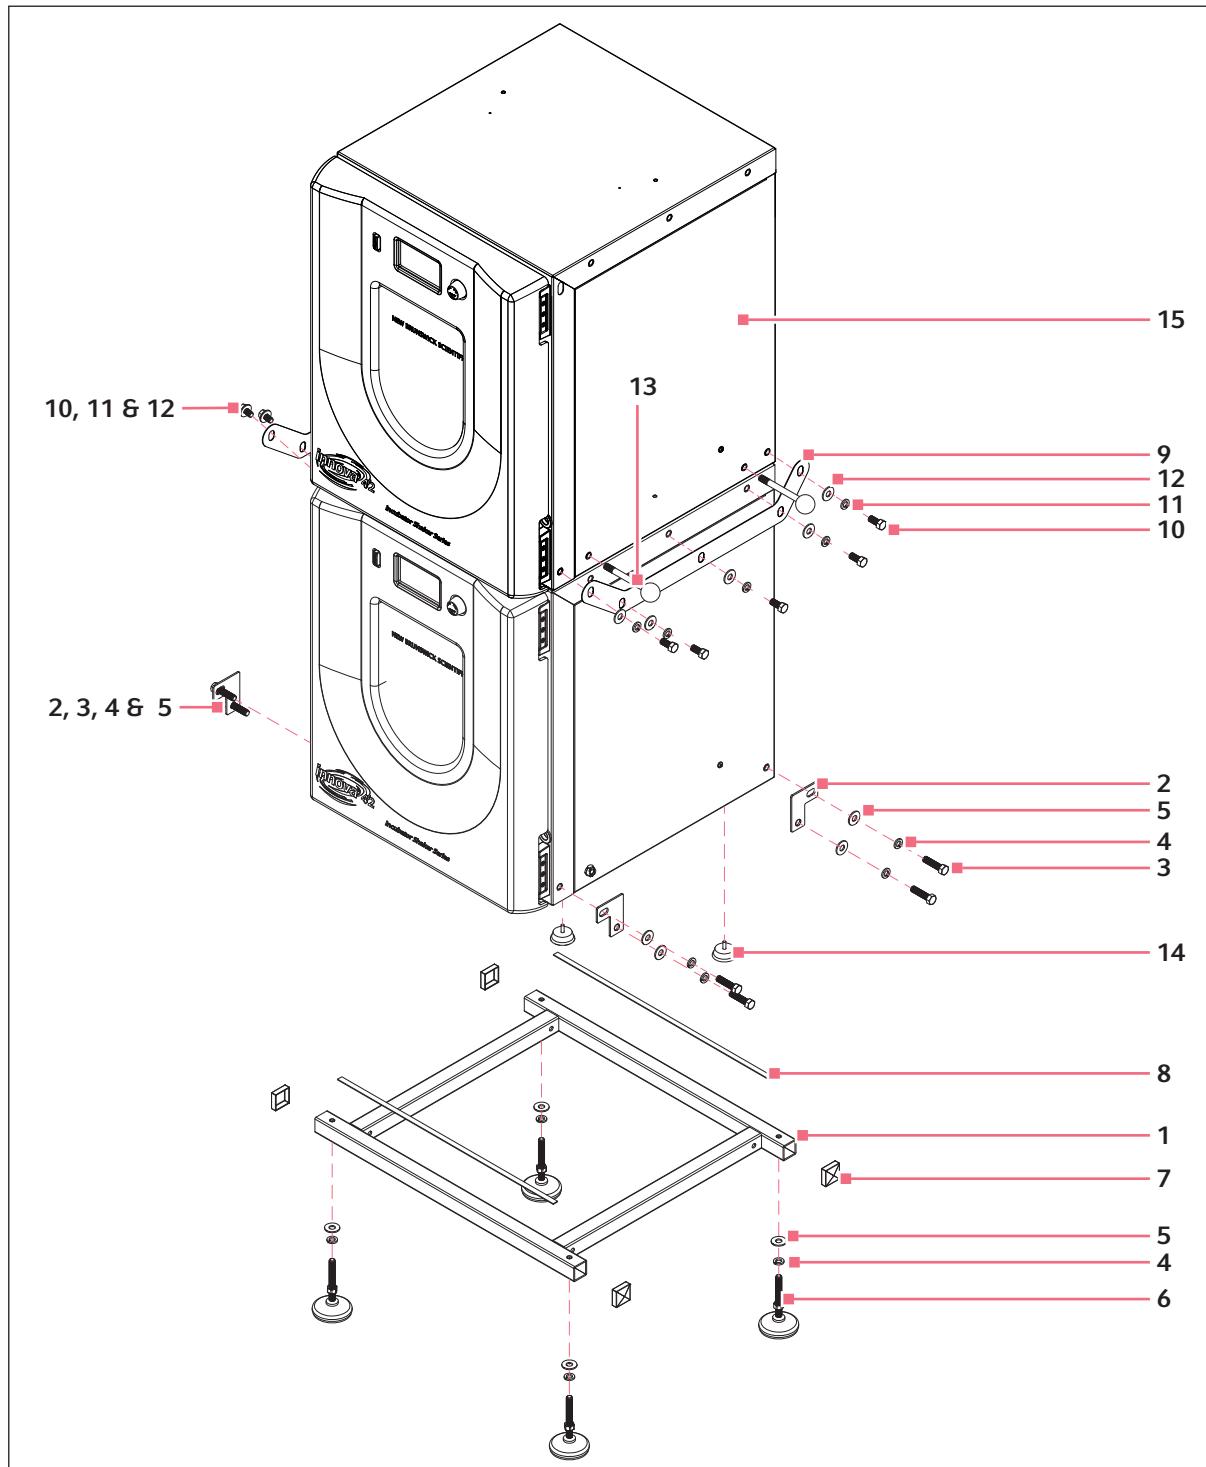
Peças do kit de empilhamento (vista explodida)
